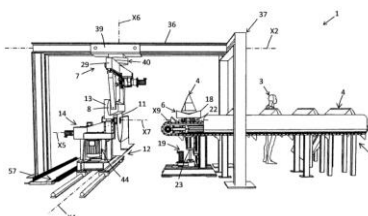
brevet « Machine de dressage de merrains » - FR3078499
